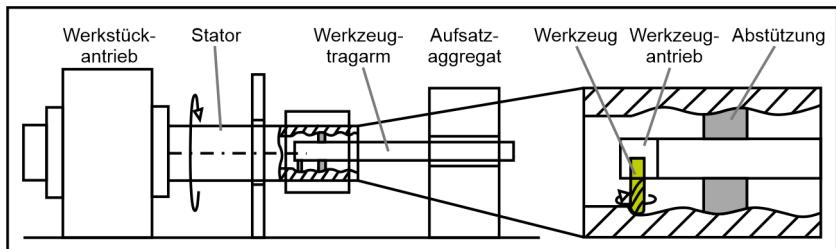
Aufbau einer Werkzeuganlage zum Innenfräsen nach [DGE*16; FJC10]
